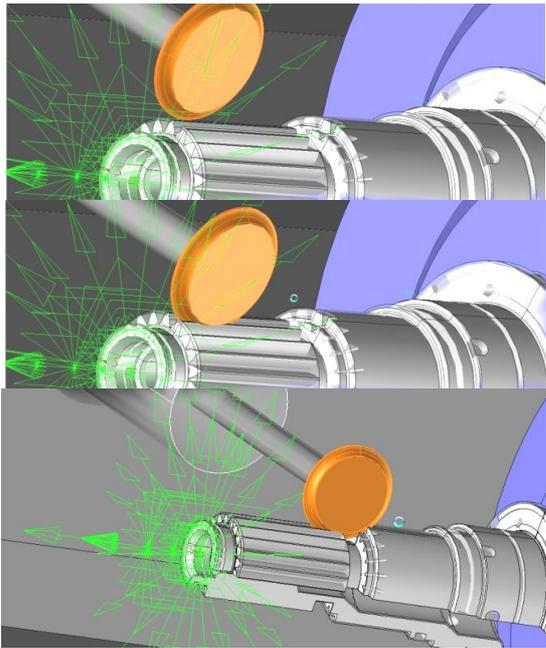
Перемещение фрезы для обработки зубьев полумуфты левой в Торсам
